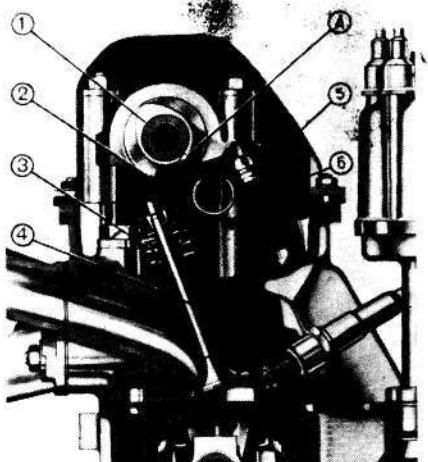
Механизм газораспределения: А — зазор между рычагом и кулачком; 1 — кулачок распределительного вала; 2 — рычаг привода клапана; 3 — маслоподжатательный колпачок клапана; 4 — клапан; 5 — регулировочный болт рычага; 6 — контргайка регулировочного болта
